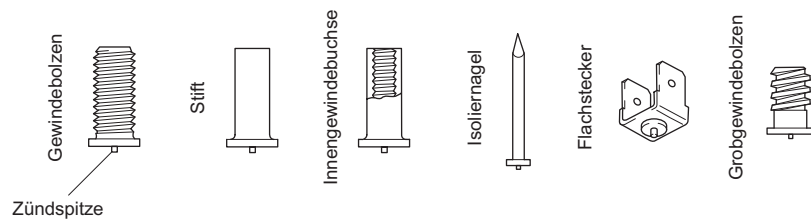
3 Einige Beispiele verschiedener Ausführungen von Schweißelementen mit Zündspitze
